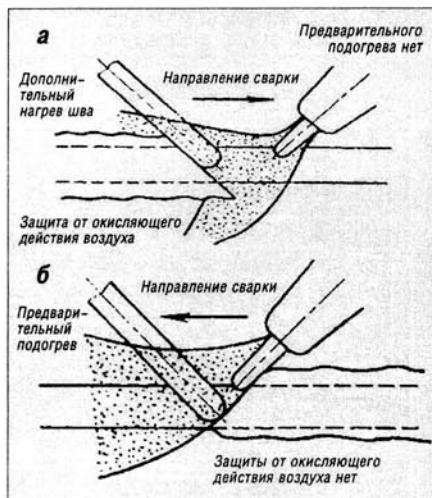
Способы газокислородной сварки (наплавки): а – правый; б – левый
